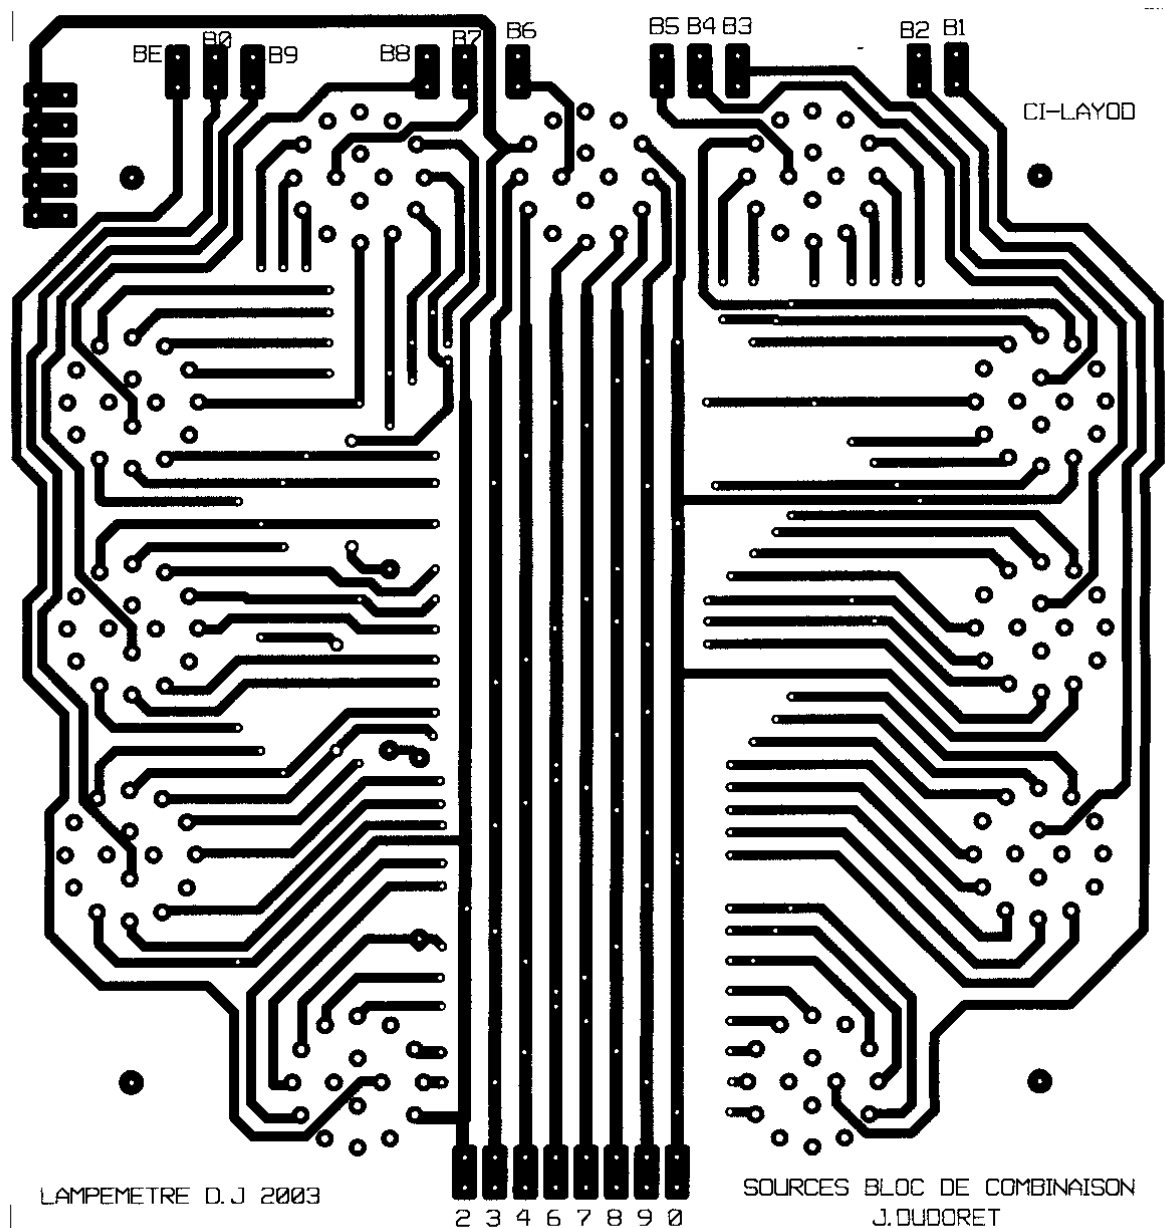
Circuit imprimé bloc de combinaison coté soudures.
